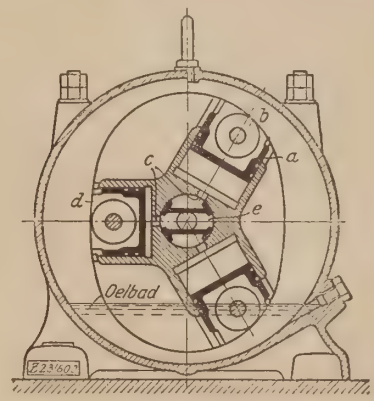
Schleuderkolbenhaspel der Gewerkschaft „Westfalia“, Lünen.
